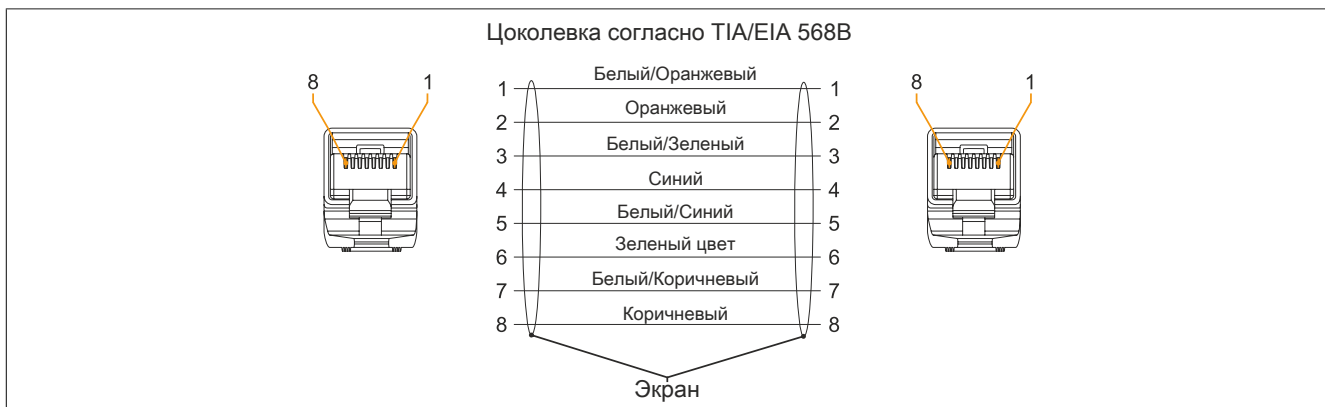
5CASD3.xxxx-00 — цоколевка
